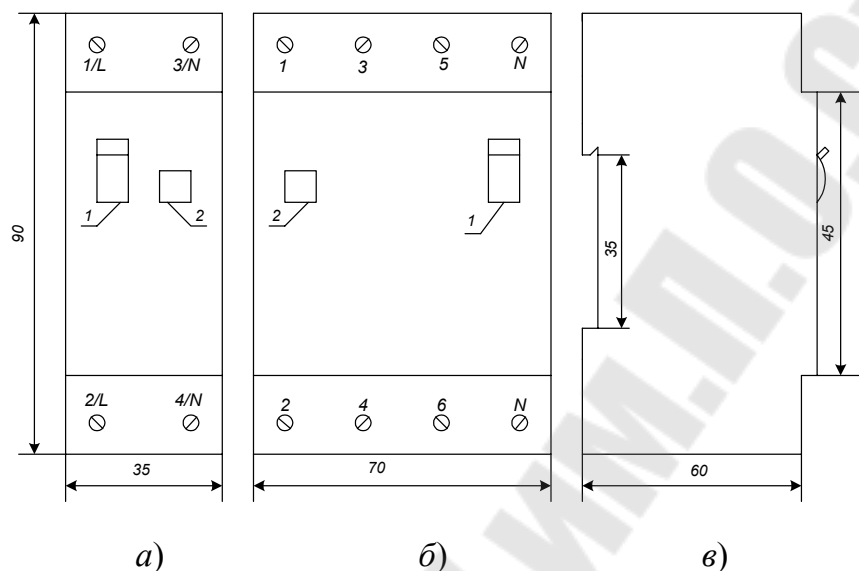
Конструктивная схема и габаритные размеры дифференциального выключателя (УЗО):
